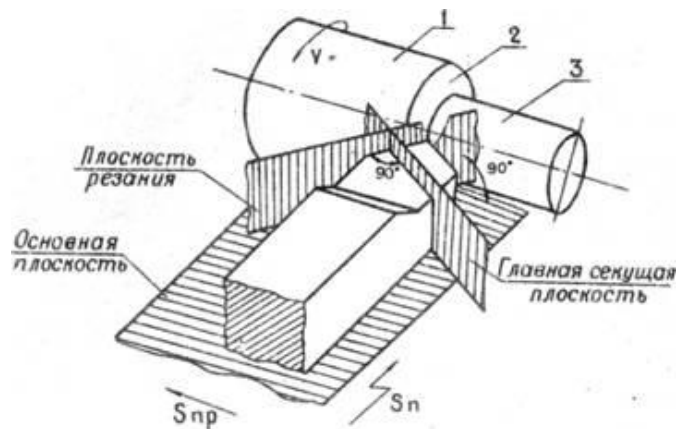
Поверхности заготовки и координатные плоскости резца. Для определения углов резца принято 5 координатных плоскостей.
